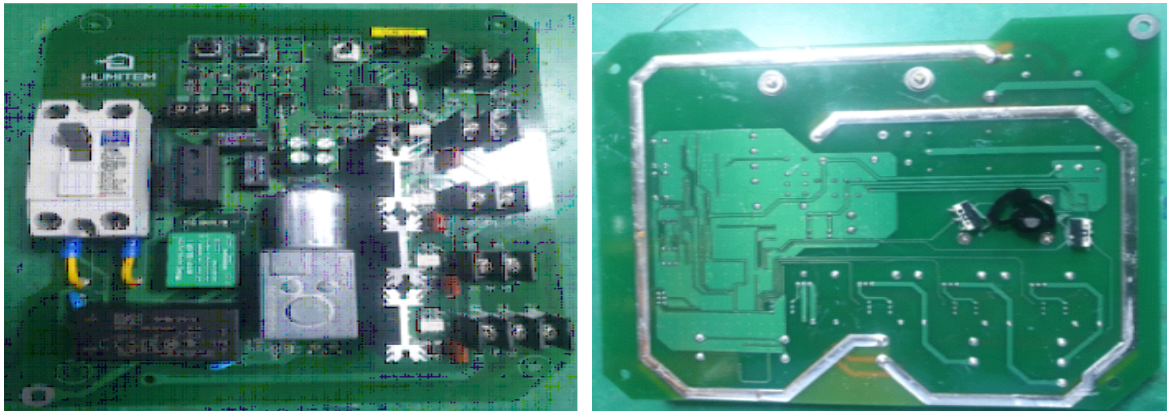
정밀 공조기 제어 PCB 설계 및 제작 (2)
